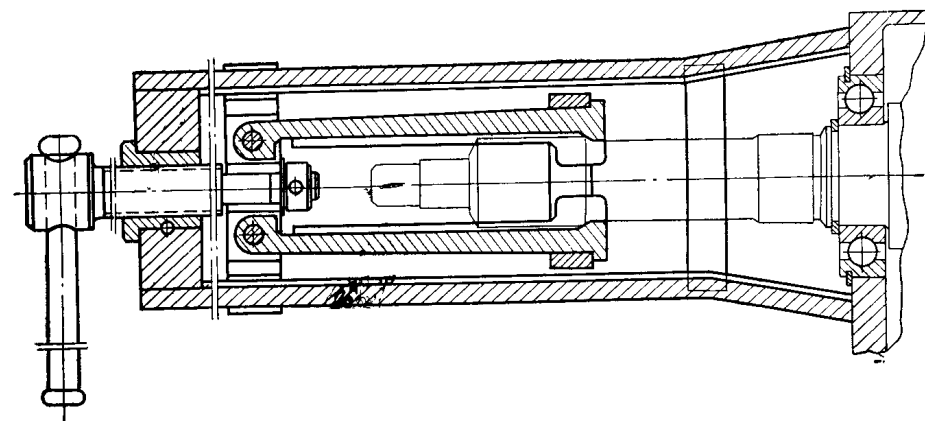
Съемник ведущего вала с подшипником из картера коробки передач
